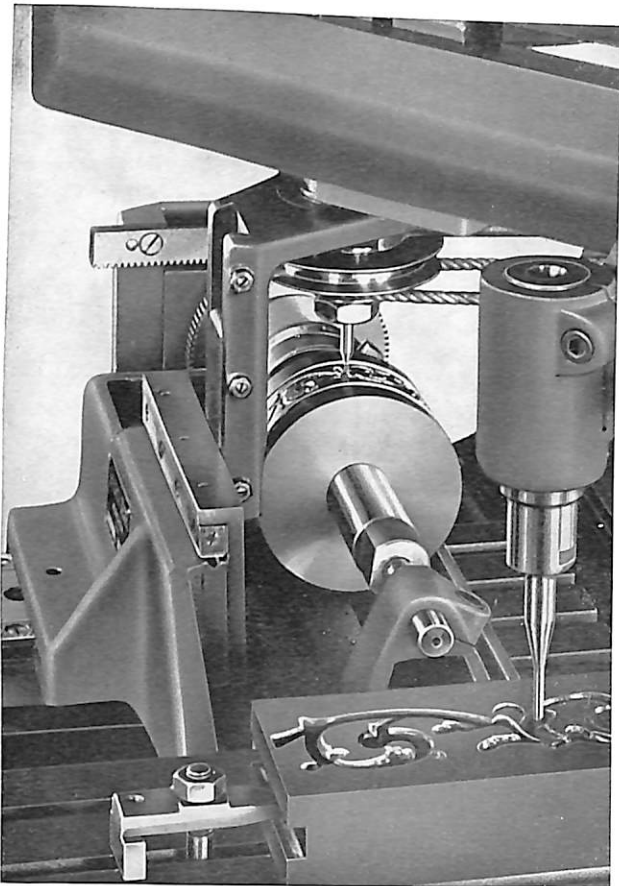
Walzengraviervorrichtungen zum Gravieren einer Bilderleistenprägerolle nach Bakelitmodell
